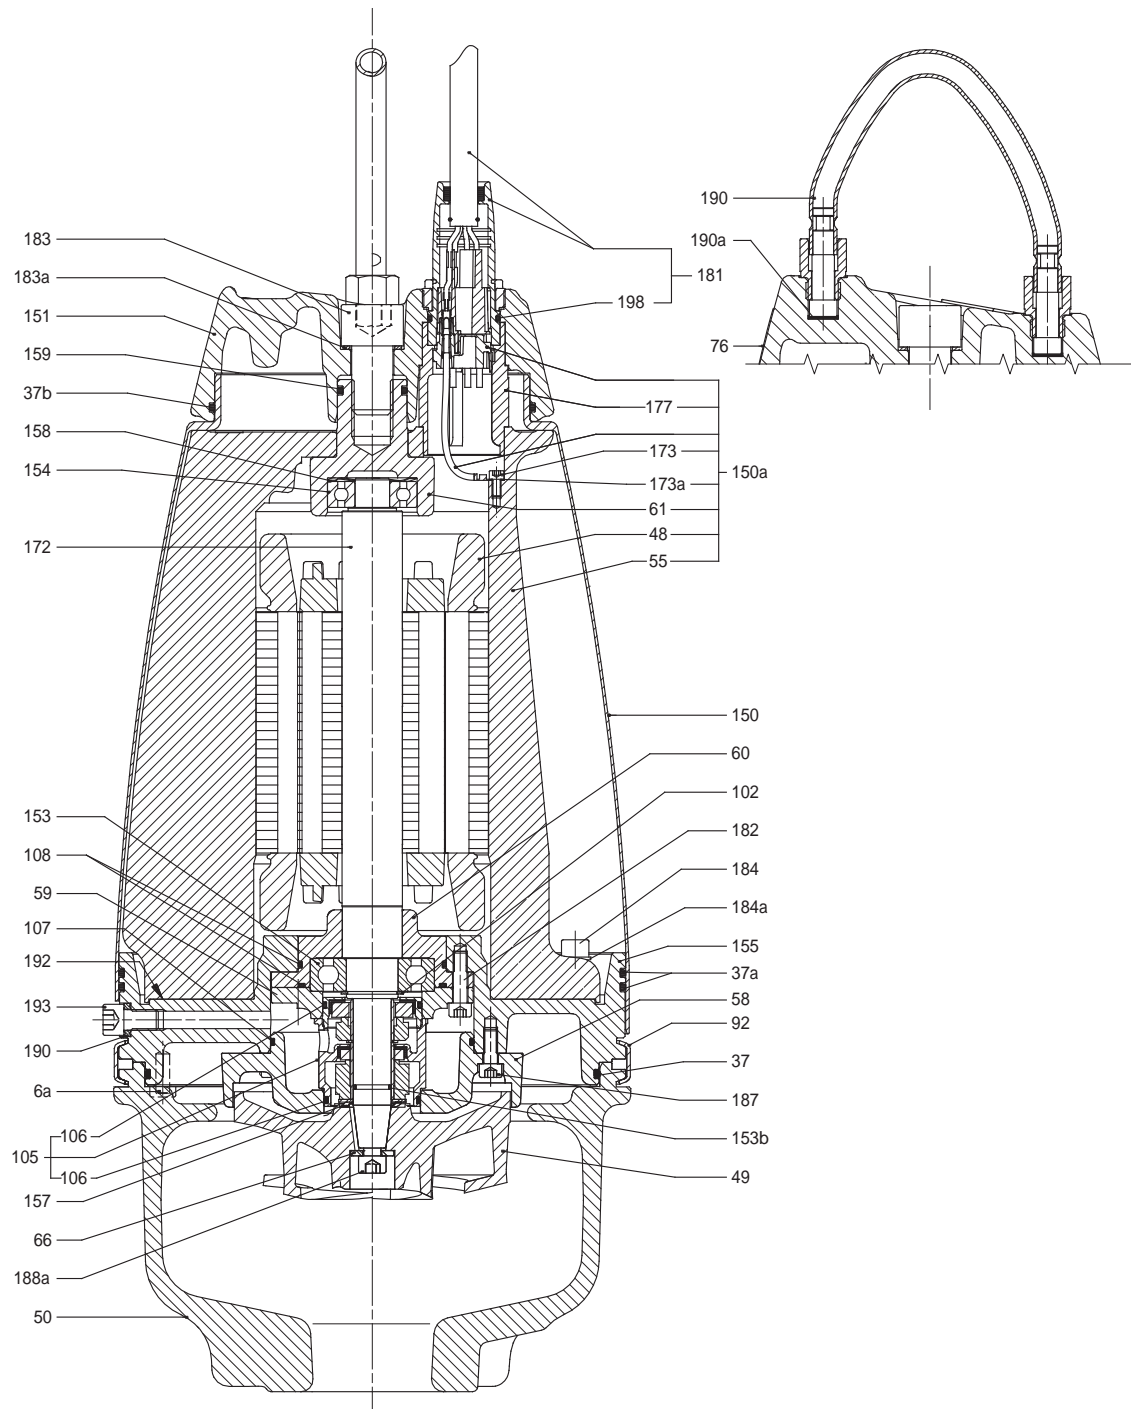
Чертеж в разрезе, насос SEV со свободно-вихревым рабочим колесом типа SuperVortex
